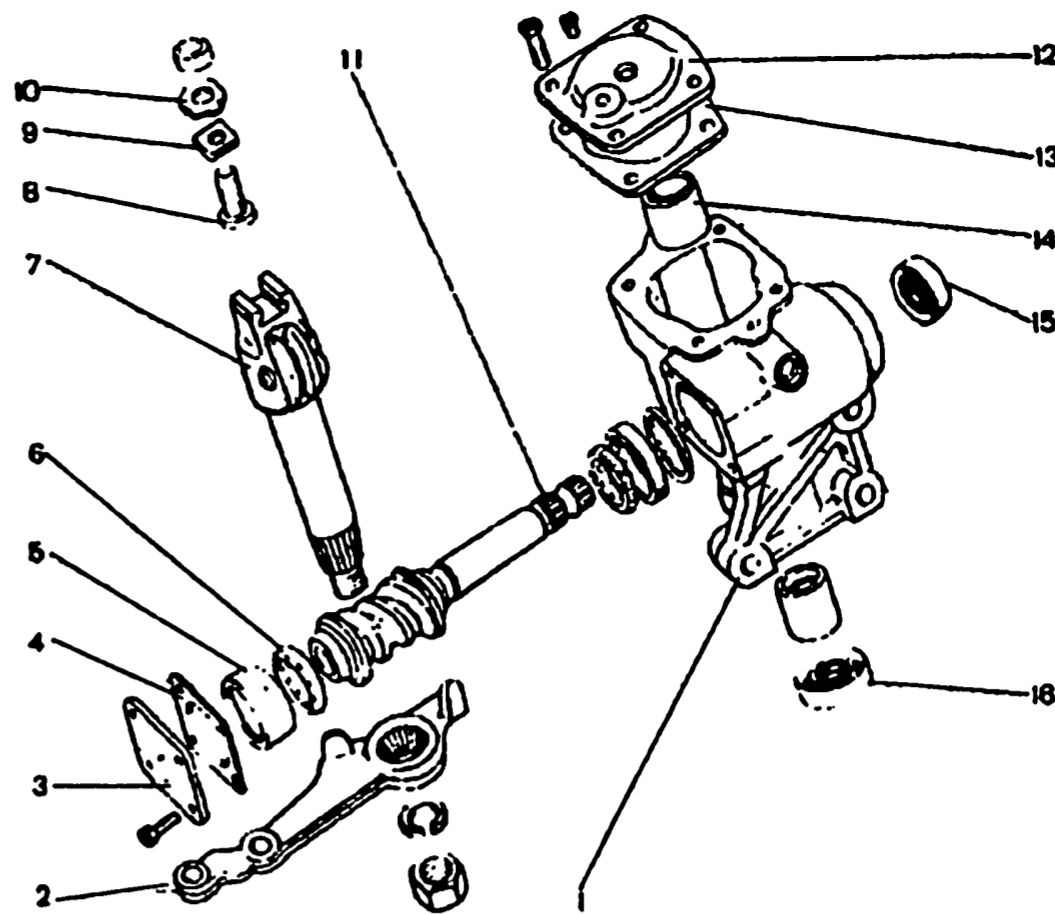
Детали картера рулевого механизма: 1 - картер; 2 - сошка; 3 - нижняя крышка картера; 4 - регулировочные прокладки; 5 - наружное кольцо подшипника вала червяка; 6 - сепаратор с шариками; 7 - вал сошки; 8 - регулировочный винт; 9 - регулировочная пластина; 10 - стопорная шайба; 11 - вал червяка; 12 - верхняя крышка картера; 13 - уплотнительная прокладка; 14 - втулка вала сошки; 15 - сальник вала червяка; 16 - сальник вала сошки
